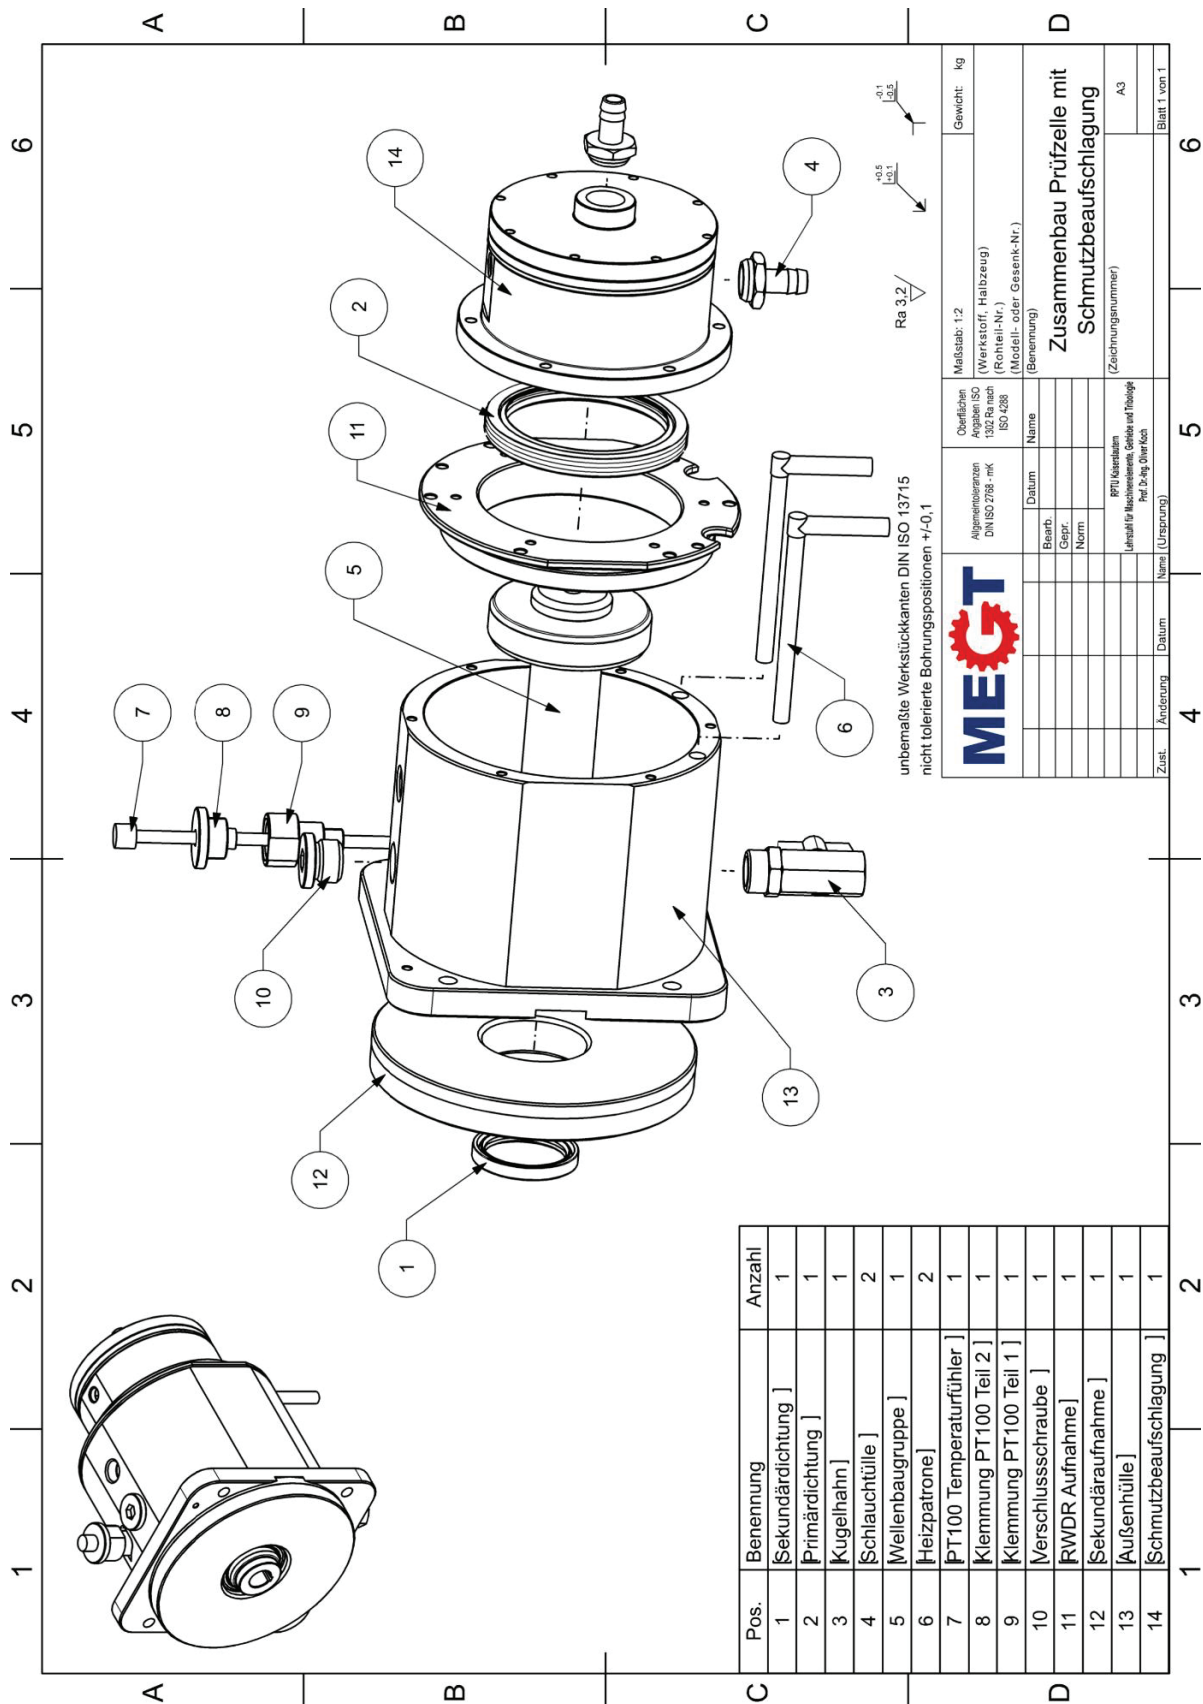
Explosionszeichnung Prüfzelle mit Beaufschlagungseinheit
